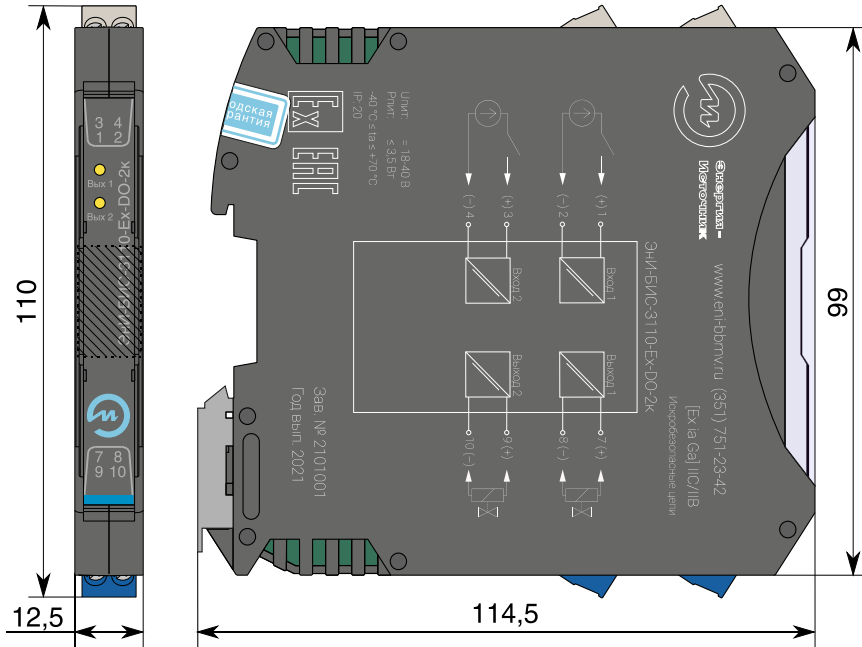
Габаритные размеры ЭНИ-БИС-3110-Ех-DO с разъемами с винтовыми клеммниками
